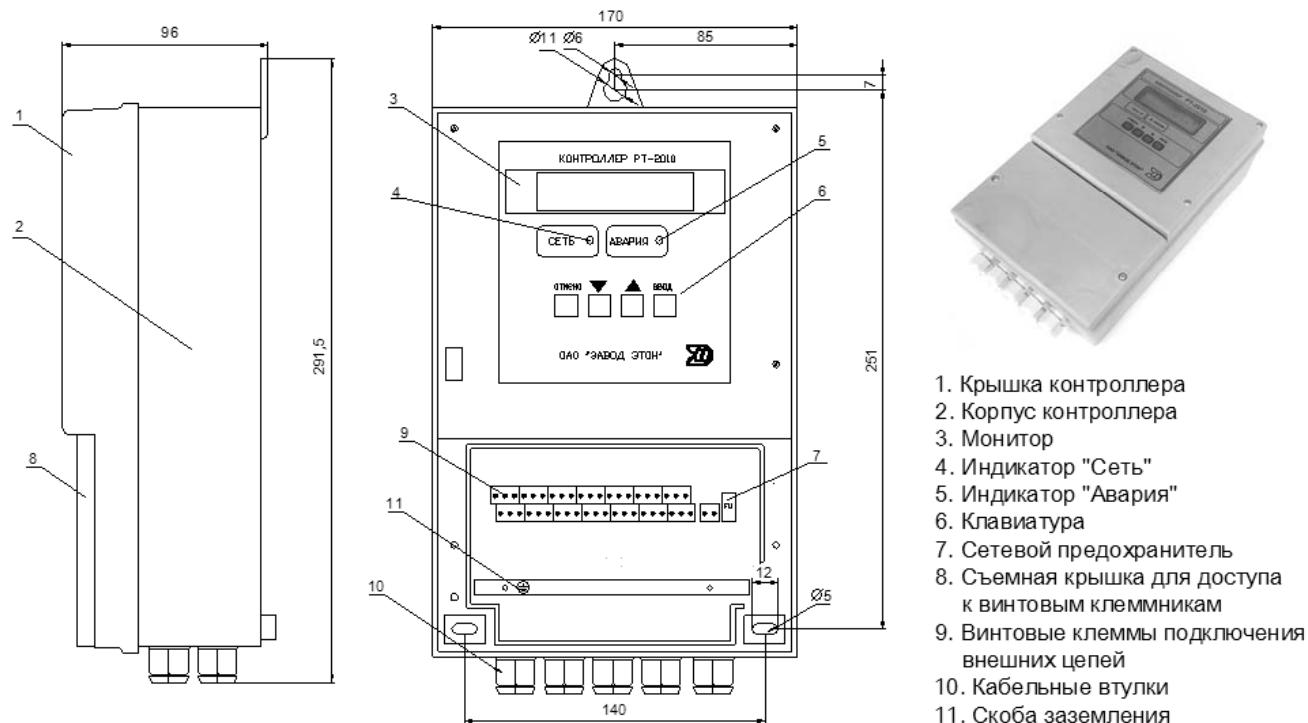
Внешний вид и общее устройство контроллера РТ-2010, габаритные и присоединительные размеры
